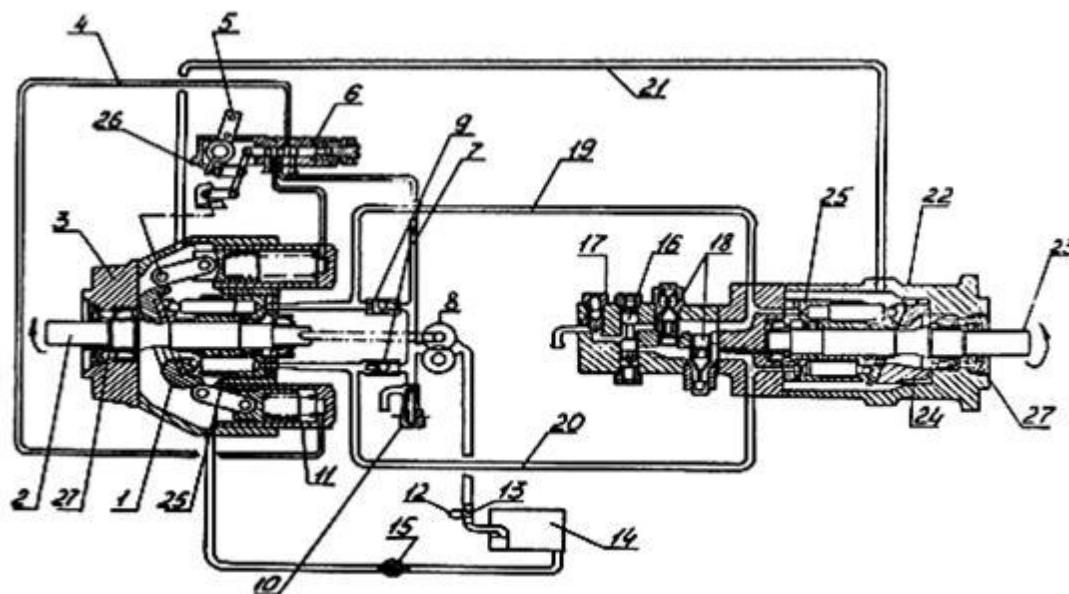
Схема гидропривода ГСТ–90: 1 — шайба; 2 — выходной вал насоса; 3 — реверсивный регулируемый насос; 4 — гидролиния управления; 5 — рычаг управления; 6 — золотник управления положением люльки; 7 — гидролиния низкого давления; 8 — насос подпитки; 9 — обратный клапан; 10 — предохранительный клапан системы подпитки; 11 — сервоцилиндр; 12 — фильтр;
